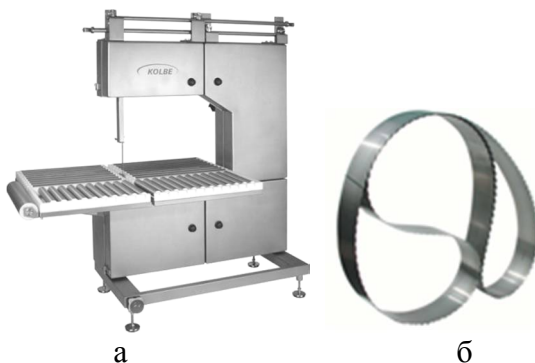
Зовнішній вигляд обладнання - стрічкопилного верстата (а) та інструмента - стрічкового полотна (б)
